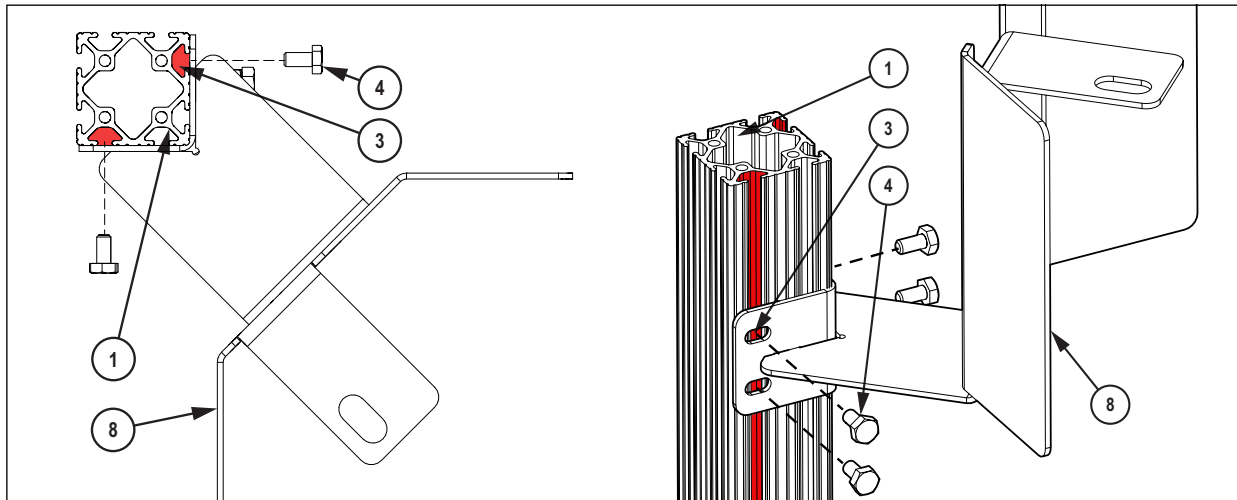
Montage der Sensorschutzvorrichtungen
